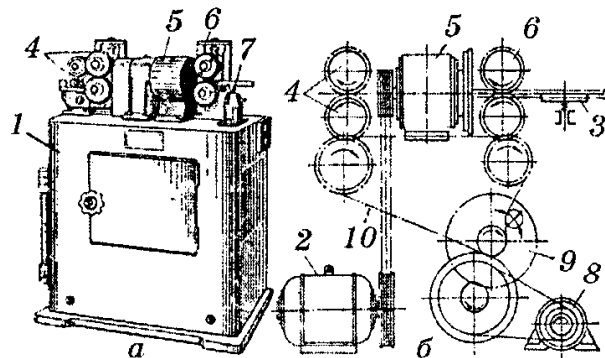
Круглопалковий верстат: *a* – загальний вигляд; *б* – кінематична схема; 1 – станина; 2 – електродвигун ножової головки; 3 – напрямний лоток; 4 – задні ролики; 5 – ножова головка; 6 – передні ролики; 7 – заготівка; 8 – електродвигун подачі; 9 – зубчаста передача; 10 – ланцюгова передача
